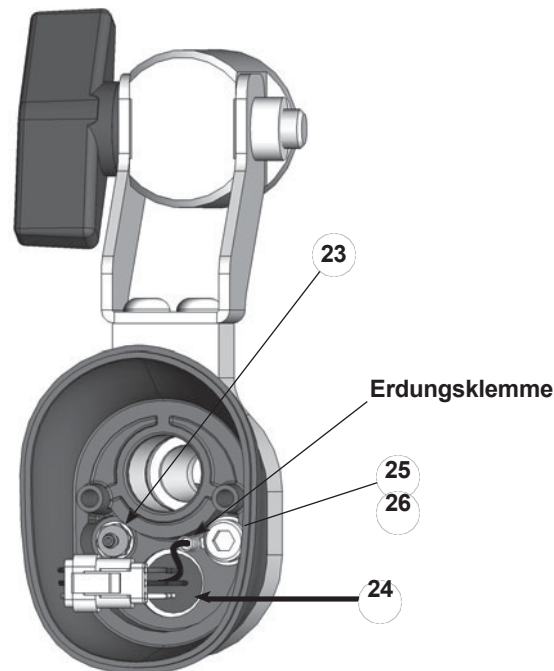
Demontage der Pistole - Austausch von Kabelbuchse und Stecknippel
